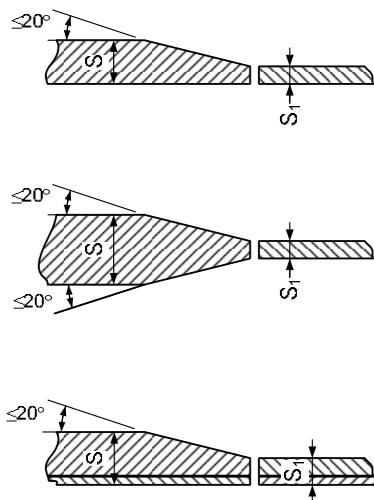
Конструкции элементов для стыковых сварных соединений разной толщины
